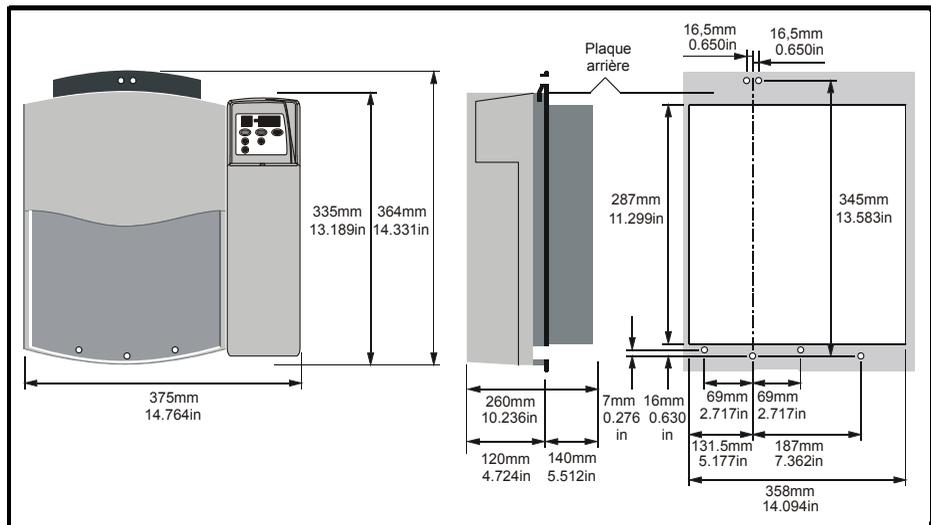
Montage sur plaque à trou de passage, unités modèle 5
